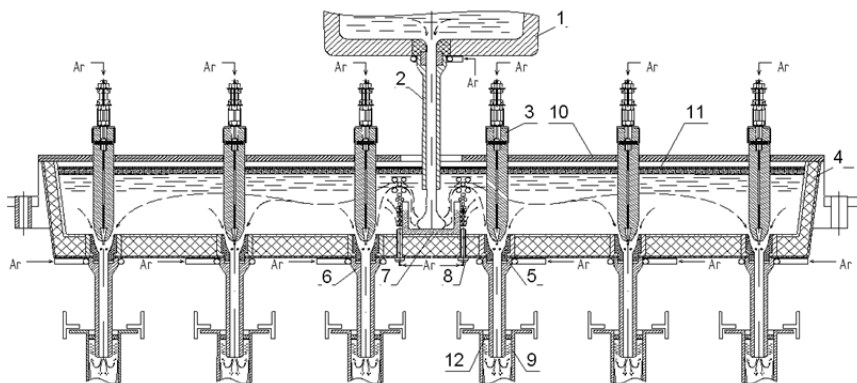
Схема подачи металла из сталковша в кристаллизаторы через промежуточный ковш:
